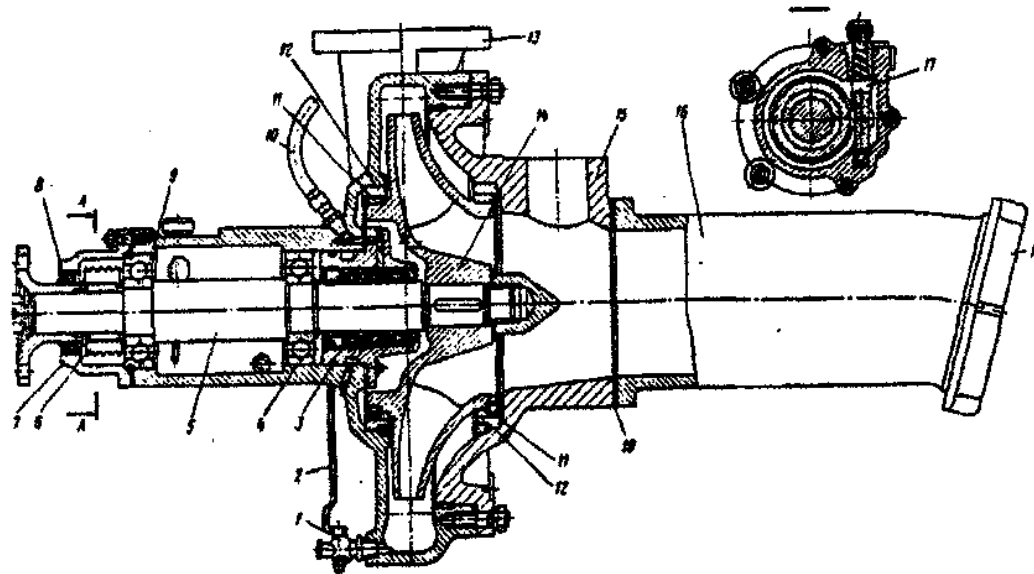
Розріз пожежного насосу ПН-40У: 1 – зливний кран; 2 – важіль; 3 – стакан; 4,9 – шарикопідшипники; 5 – вал; 6 – черв'як; 7 – корпус приводу тахометра; 8 – сальник; 10 – діоритовий шланг; 11,12 – ущільнювальні кільця; 13 – корпус; 14 – робоче колесо; 15 – кришка; 16 – всмоктувальний патрубок; 17 – черв'ячне колесо; 18 – заглушка; 19 – прокладка
